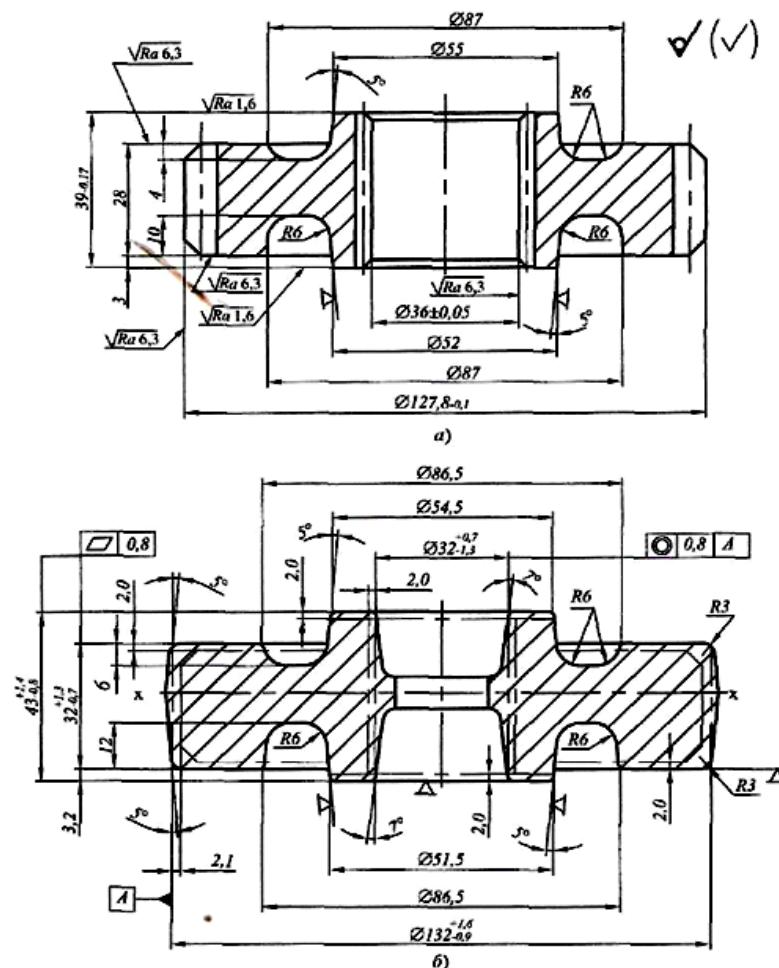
Деталь-«шестерня»(а) и штампованная заготовка на КГШП (б).
